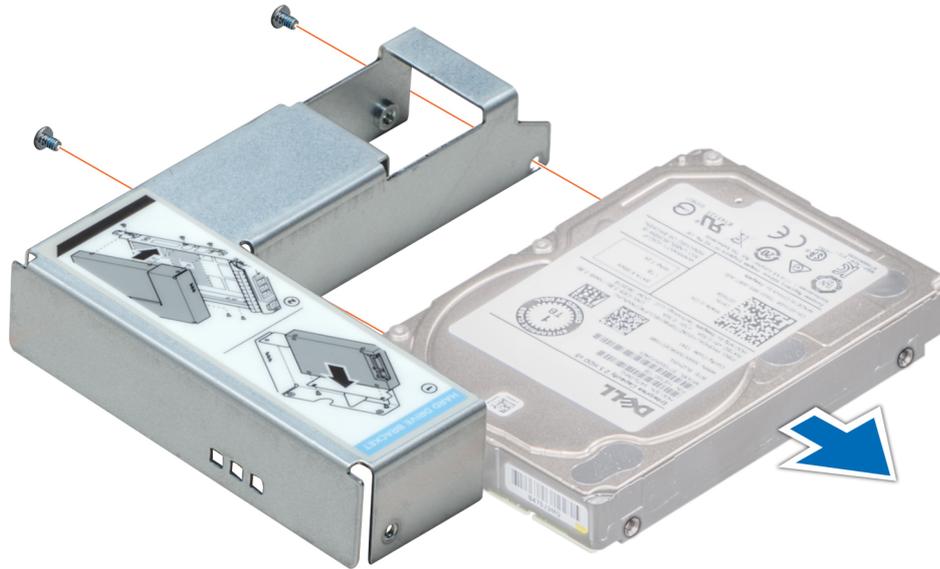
Entfernen eines 2,5-Zoll-Laufwerks aus einem 3,5-Zoll-Laufwerkadapter
